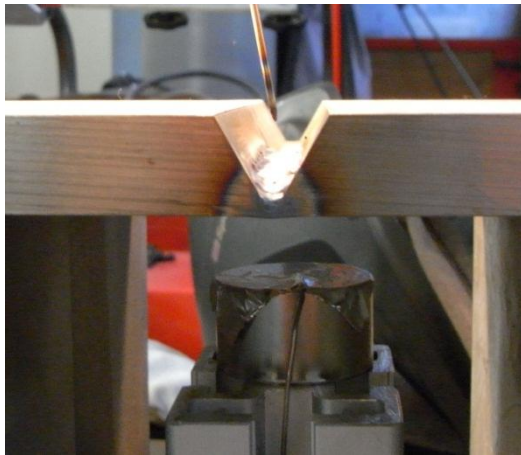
Anordnung des Permanentmagnetes unter der Schweißnahtunterseite (Luftspalt 20 mm), die Nachführung erfolgte mit der Bahnsteuerung parallel zum Schweißbrenner.
